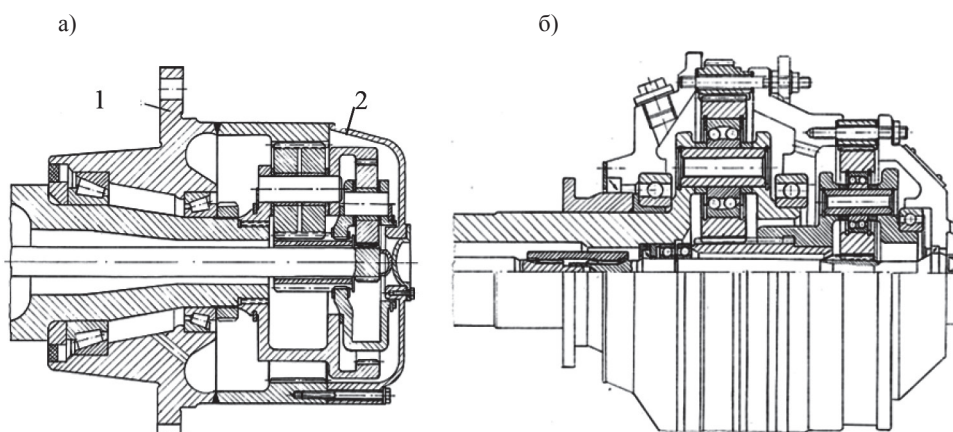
Конструкции специальных редукторов: а — редуктор с опорным звеном, входящим в один механизм; б — редуктор с опорным звеном, входящим в оба механизма
